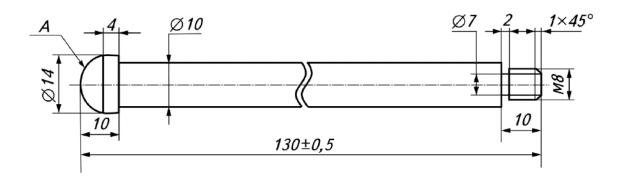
Рукоятка для винтового зажима столярного верстака
